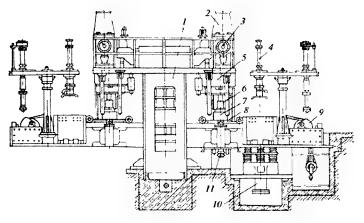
Автоматический формовочный агрегат АФА-9:
